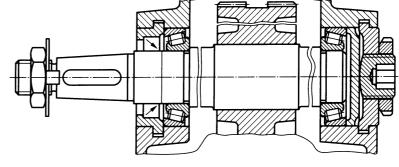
Выходной вал шевронного редуктора (мотор-редуктора)
